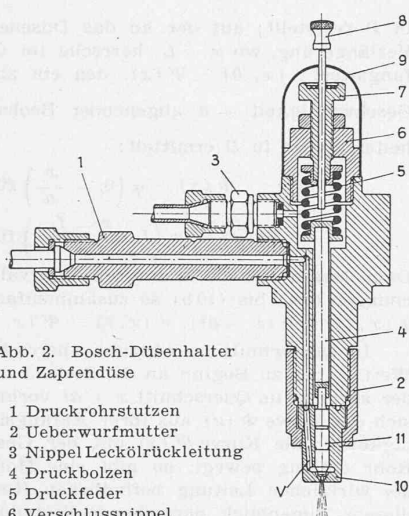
Bosh-Düsenhalter und Zapfendüse
